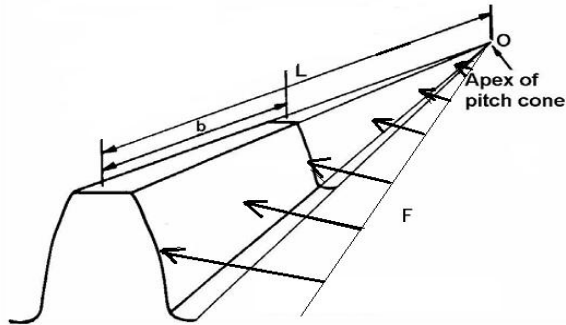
Distribusi gaya pada *bevel gear* [1]
